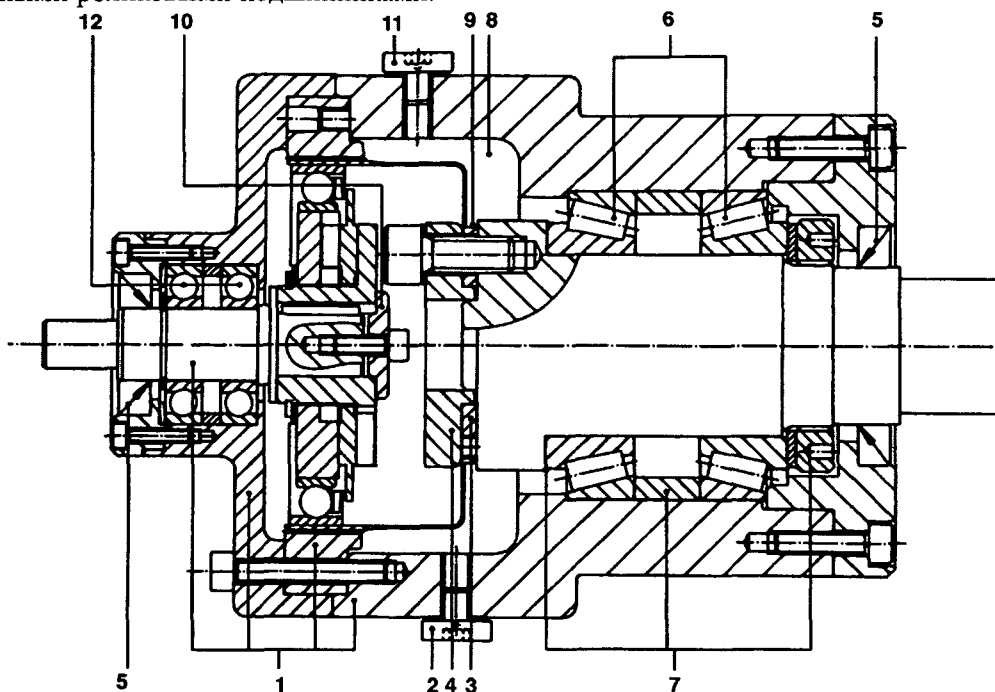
Волновая передача (Harmonic Drive GmbH): 1 – скоростной вал; внешнее опорное колесо и корпус; 2 – выходное отверстие для масла, 3 – гибкое колесо, 4 – прижимное кольцо, 5 – уплотнение тихоходного вала, 6 – роликовые подшипники тихоходного вала, 7 – гайка и распорные кольца для регулирования правильного осевого положения гибкого колеса, 8 – воздушный вентиляционный канал, 9 – гибкое колесо, 10 – опорная шайба крепления волнового генератора на скоростном валу, 11 – пробка для заливки масла, 12 – шариковые подшипники скоростного вала
